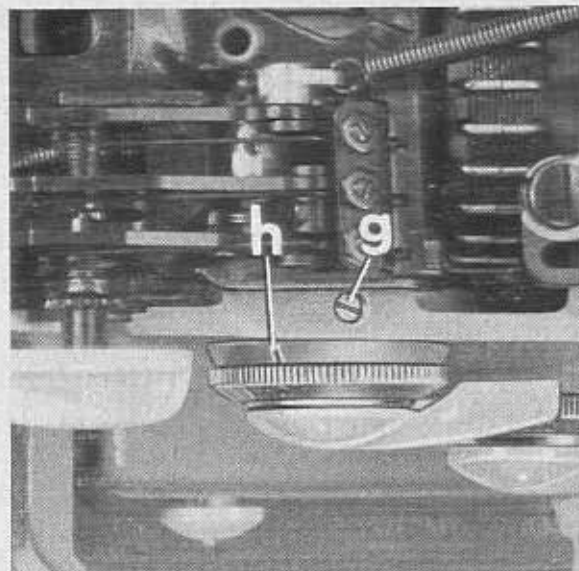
Befestigungsschraube g und Einstellstrich h für die Justierung Seite 66.
